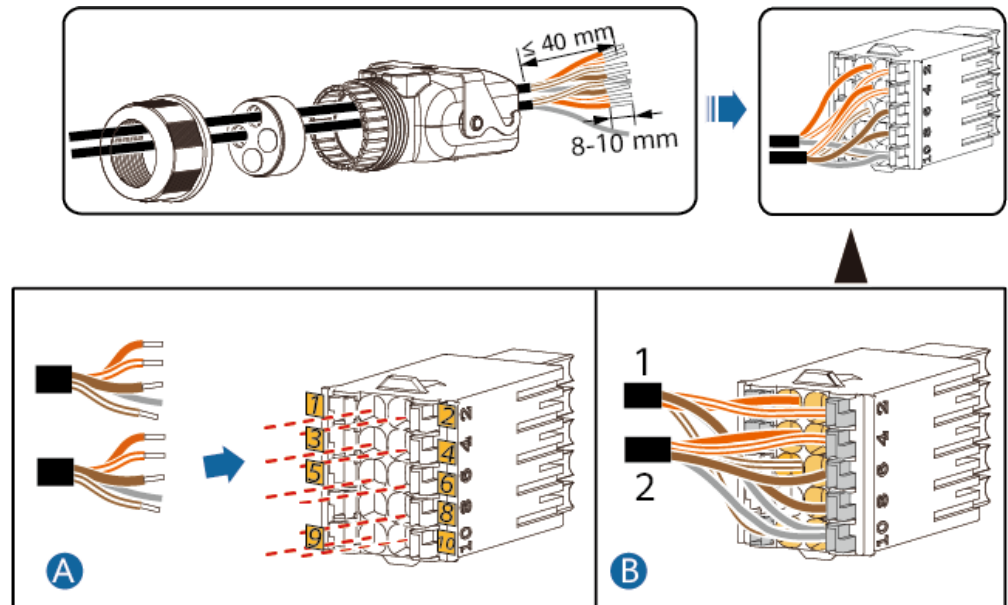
Installazione del cavo (collegamento a SmartGuard)
